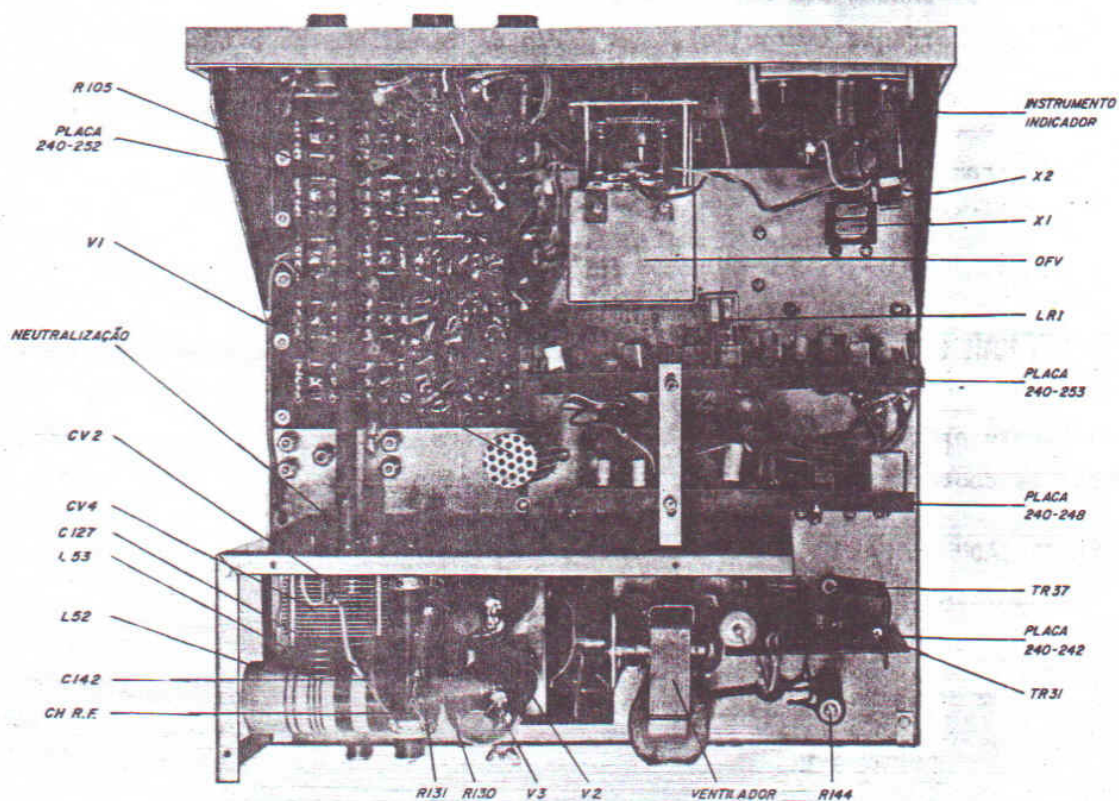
VISTA DA PARTE SUPERIOR DO CHASSI
